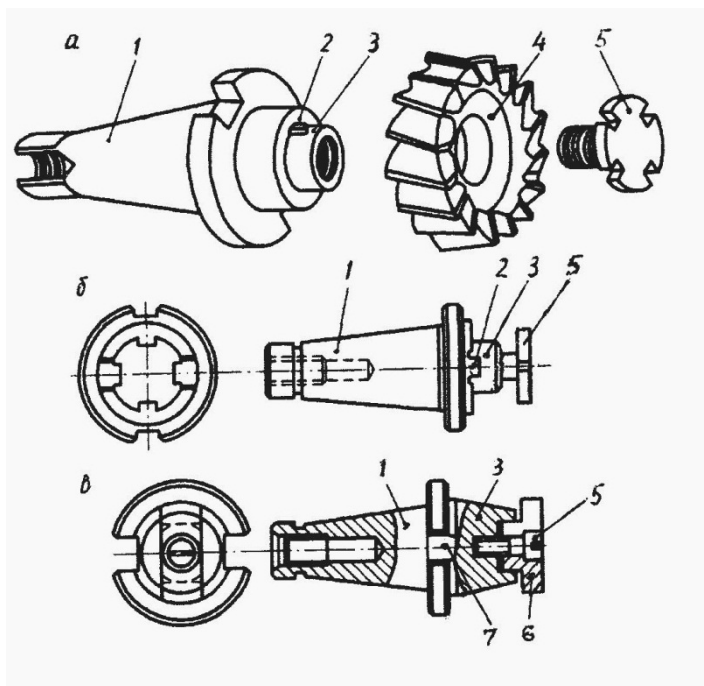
Установка торцевых фрез на шпинделях станка: 1 — конические хвостовики; 2 — шпонки; 3 — посадочные шейки; 4 — фреза; 5 — винты; 6 — шайба; 7 вкладыш
